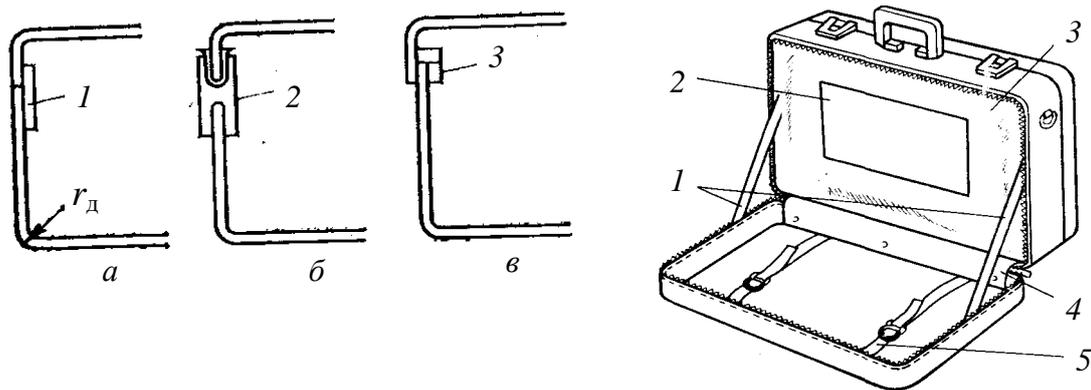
Расположение крышки и корпуса чемодана: 1-фланец; 2—кранец; 3—рамка; r_d —радиус закругления
